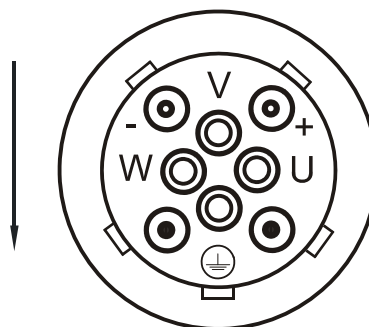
Motorgegenstecker für die SM-Serie (Gewinde M40)
